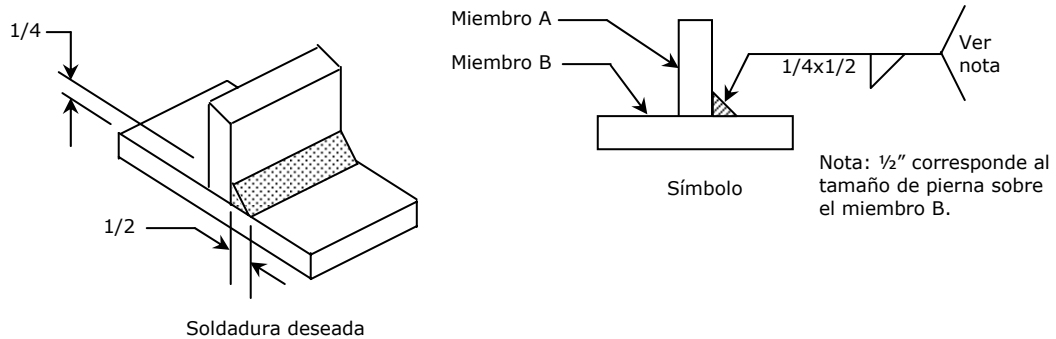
Soldadura de filete que aplica del lado al que apunta la flecha
